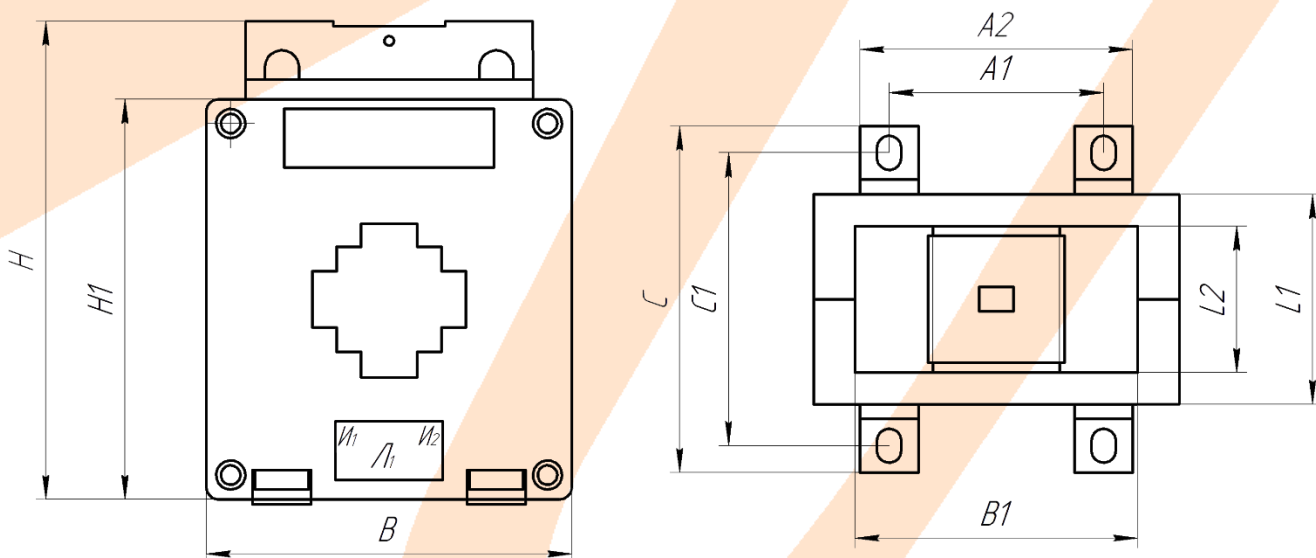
Габаритные и установочные размеры трансформаторов ТШП -0,66
